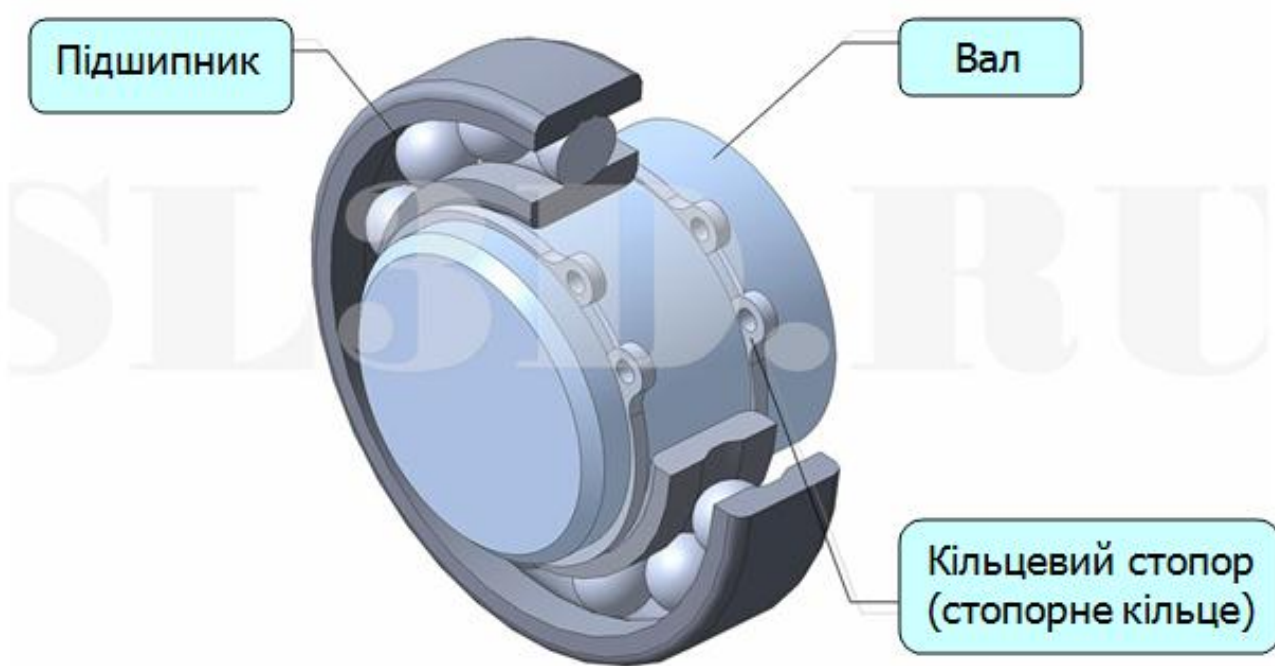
Установка підшипника з фіксацією кільцевими стопорами
